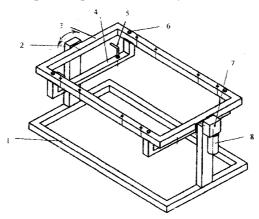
Стенд: 1 — основание; 2 — стойка; 3 — рама; 4 — кранштейн; 5 — крепление к детали; 6— болт крепления кронштейна; 7 — червячный редуктор; 8 — электродвигатель
